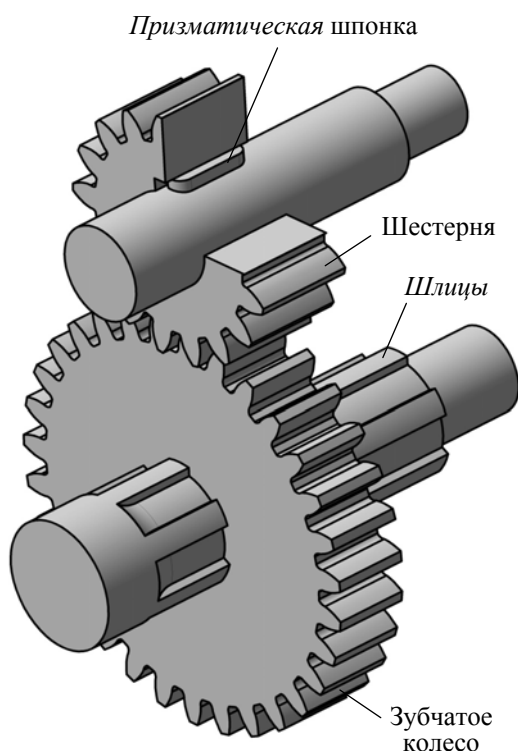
Соединение валов с зубчатыми колесами посредством конструктивных элементов – призматической шпонки и шлицев
